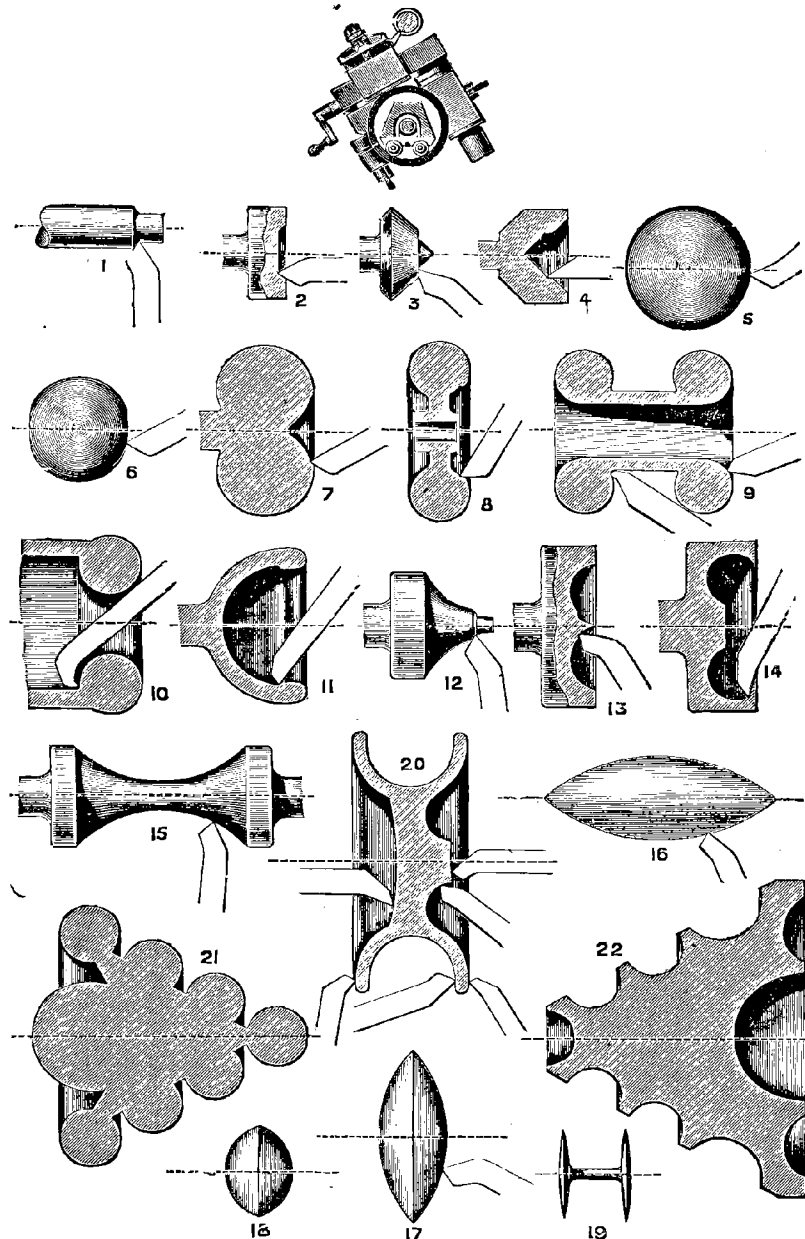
Opérations de tournage pouvant être exécutées avec la machine universelle à travailler les métaux.
